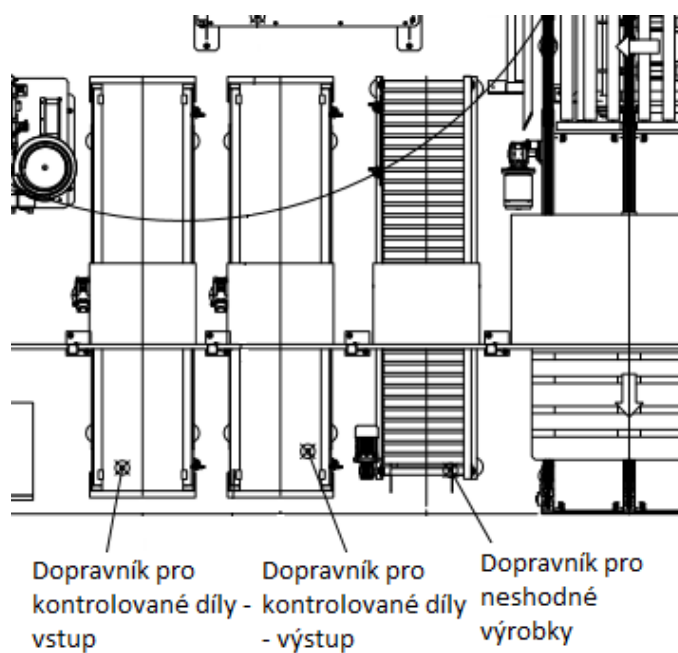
Buňka pro odjehlení a montáž pohled shora
